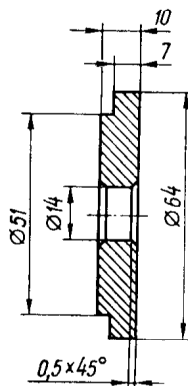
Оправка для выпрессовки наружного подшипника ведомого вала колесного редуктора
